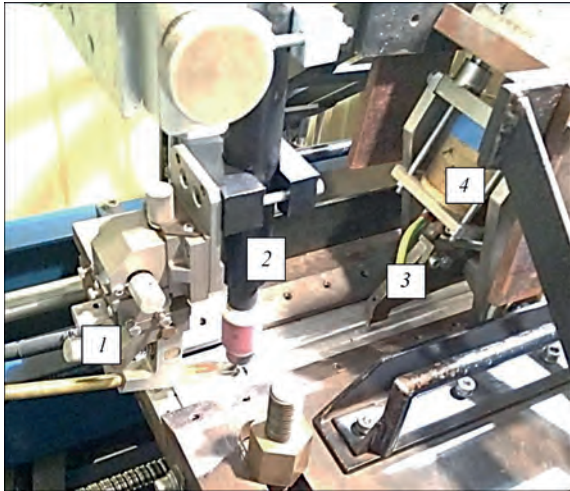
Апаратний комплекс для автоматичного зварювання TIG, яке є сумісним із ЕДО зварного шва: 1 – система для подання присадного дроту; 2 – пальник для зварювання; 3 – електродний пристрій; 4 – лінійний соленоїд переміщення електрода ЕДО обробки, що забезпечували енергію однократної електродинамічної дії на рівні 1 кДж.
